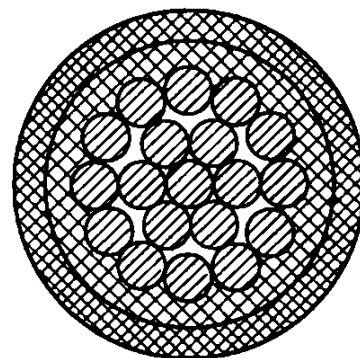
Поперечный разрез одножильного кабеля марки КНРУ
